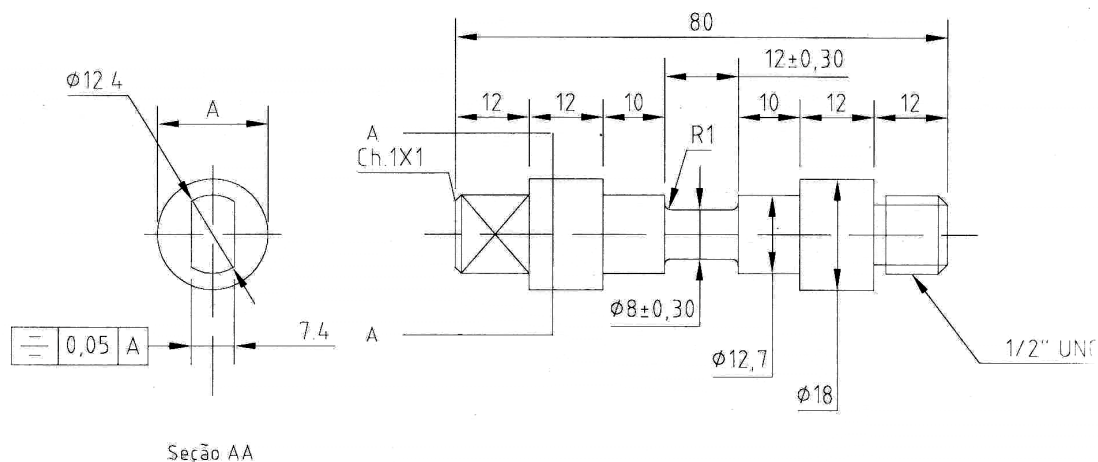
Desenho do corpo de prova utilizado para o ensaio de torção.
